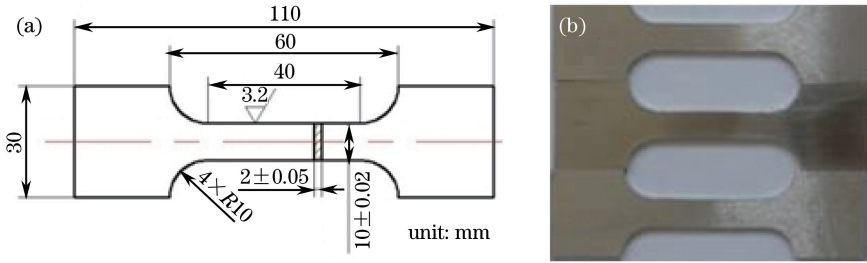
(a) 拉伸性能测试试样尺寸; (b) 拉伸试样
